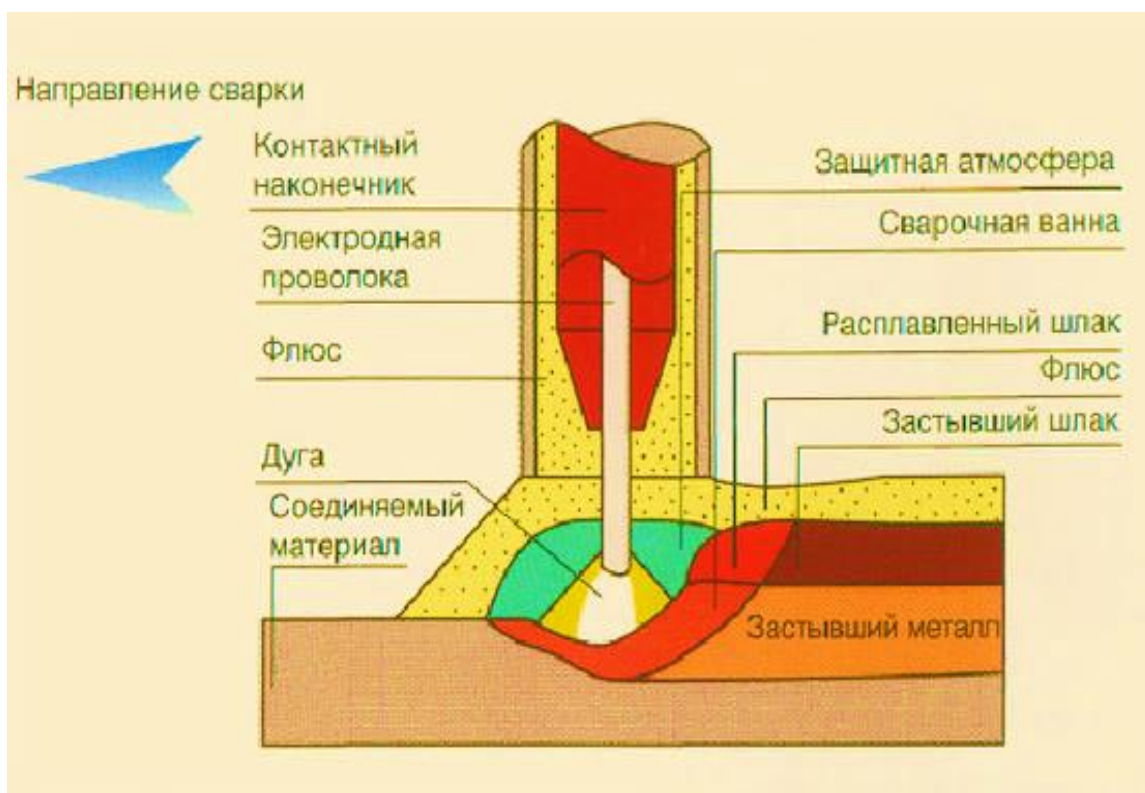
Схема процесса автоматической дуговой сварки под флюсом:
